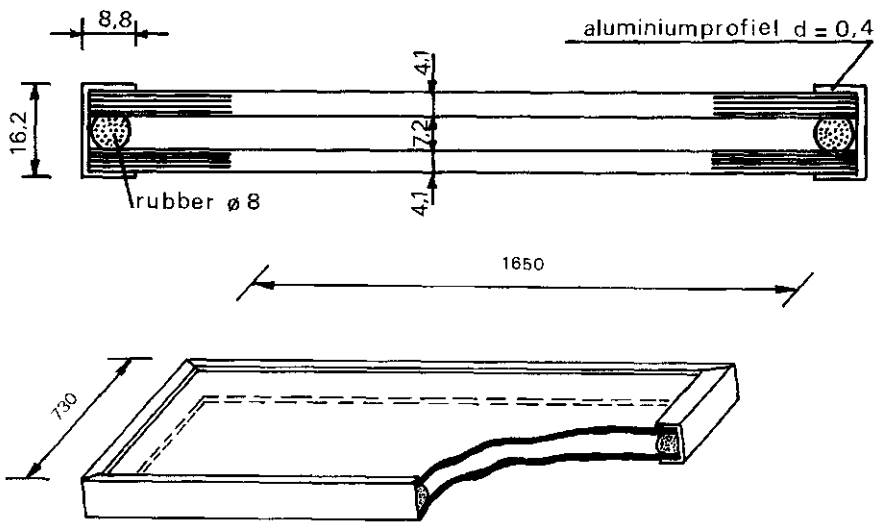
Details van de constructie van de meetkas; zie voor doorsneden afbeelding 1: bovenaanzicht (dek) en zijaanzicht (langsgevel), en afbeelding 2: doorsnede A-A.
